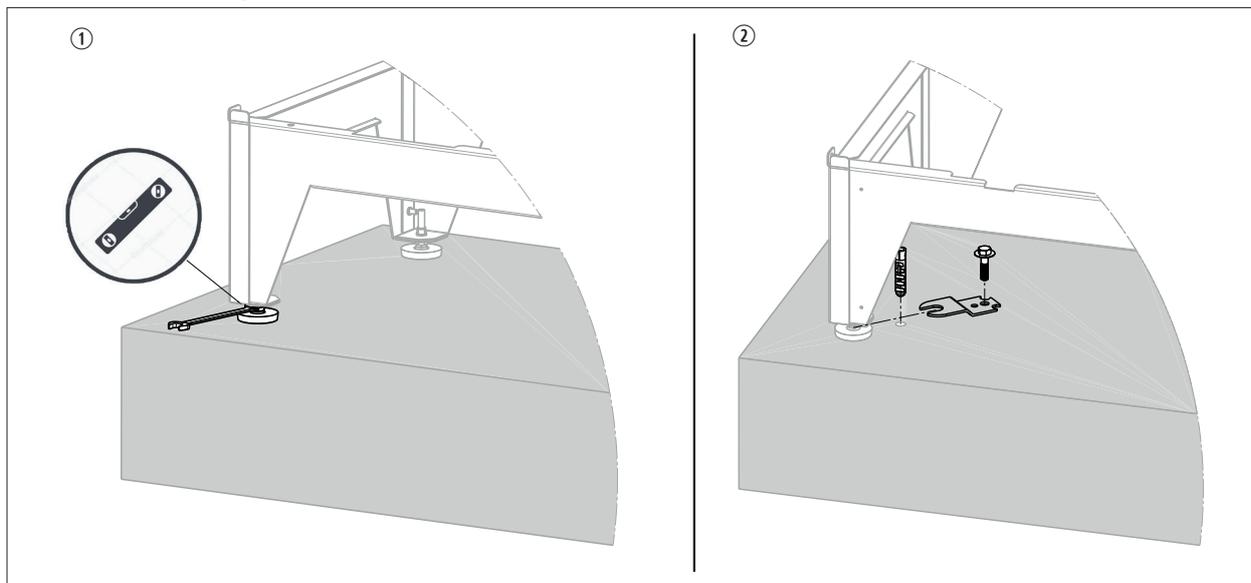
Montare il rialzo a pavimento sul basamento
